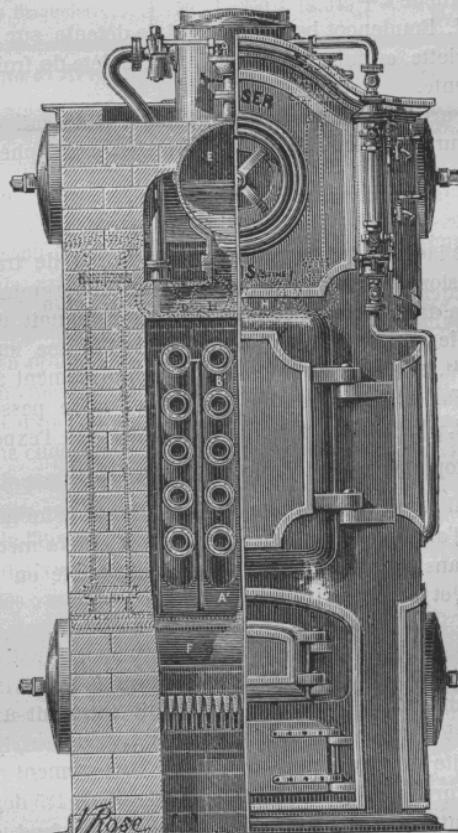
Coupe transversale et vue de la façade extérieure.
